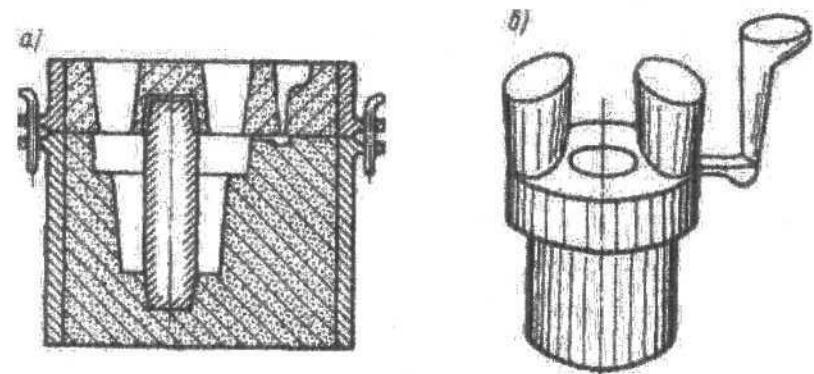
Литьевая форма для стальной отливки (а) и отливка с литниковой системой (б)
